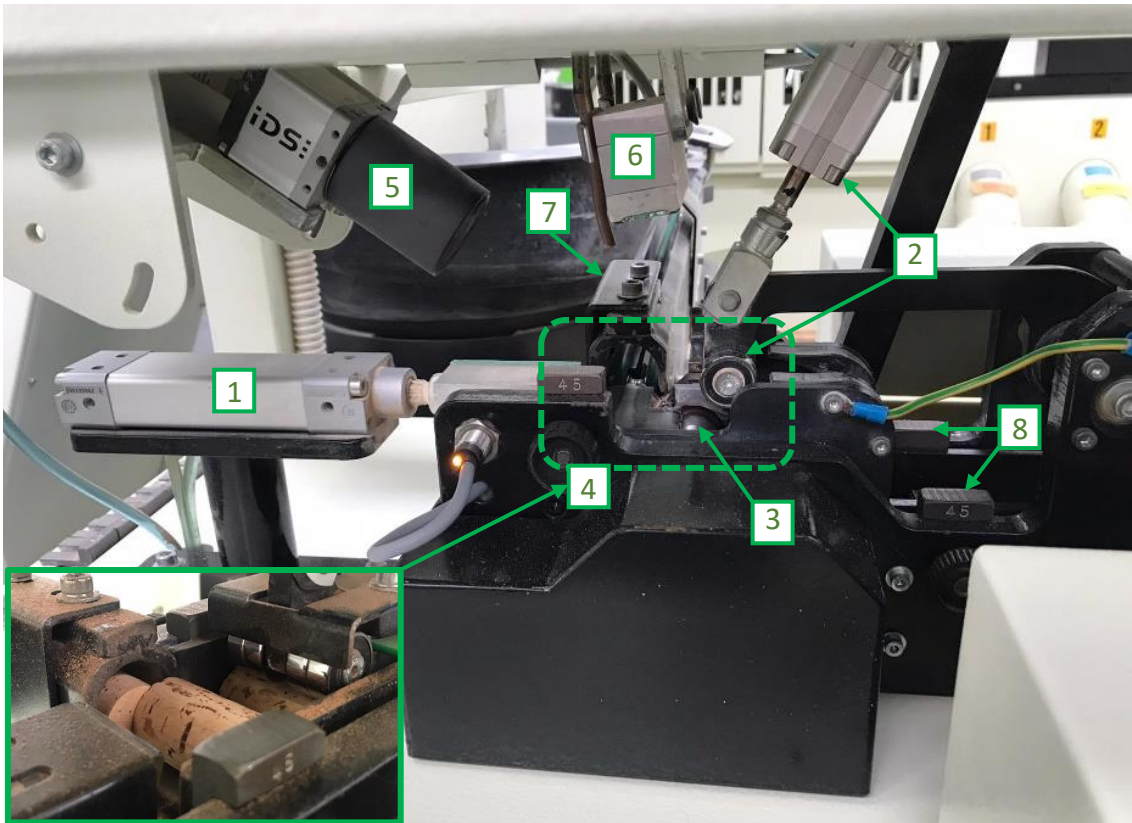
Interior do equipamento de escolha eletrónica (parte 1)
